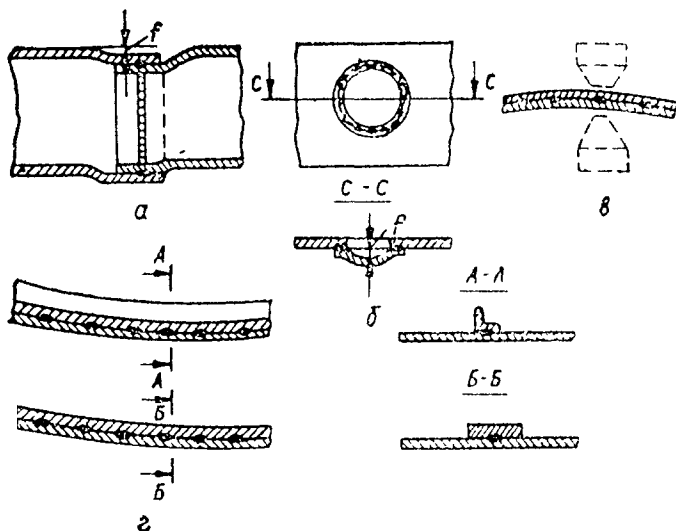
Деформация деталей (изделий) при контактной сварке: а — уменьшение диаметра изделия в зоне сварного шва; б — потеря устойчивости участка, окруженного швом; в — неравномерность нагрева из-за различной контактной площади электрода; г — деформация вследствие сварки деталей различного сечения
